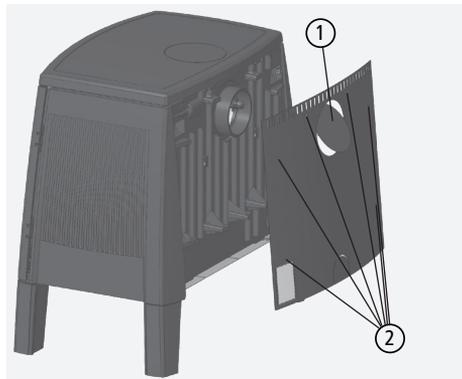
ôter la tôle prédécoupé à l'arrière
